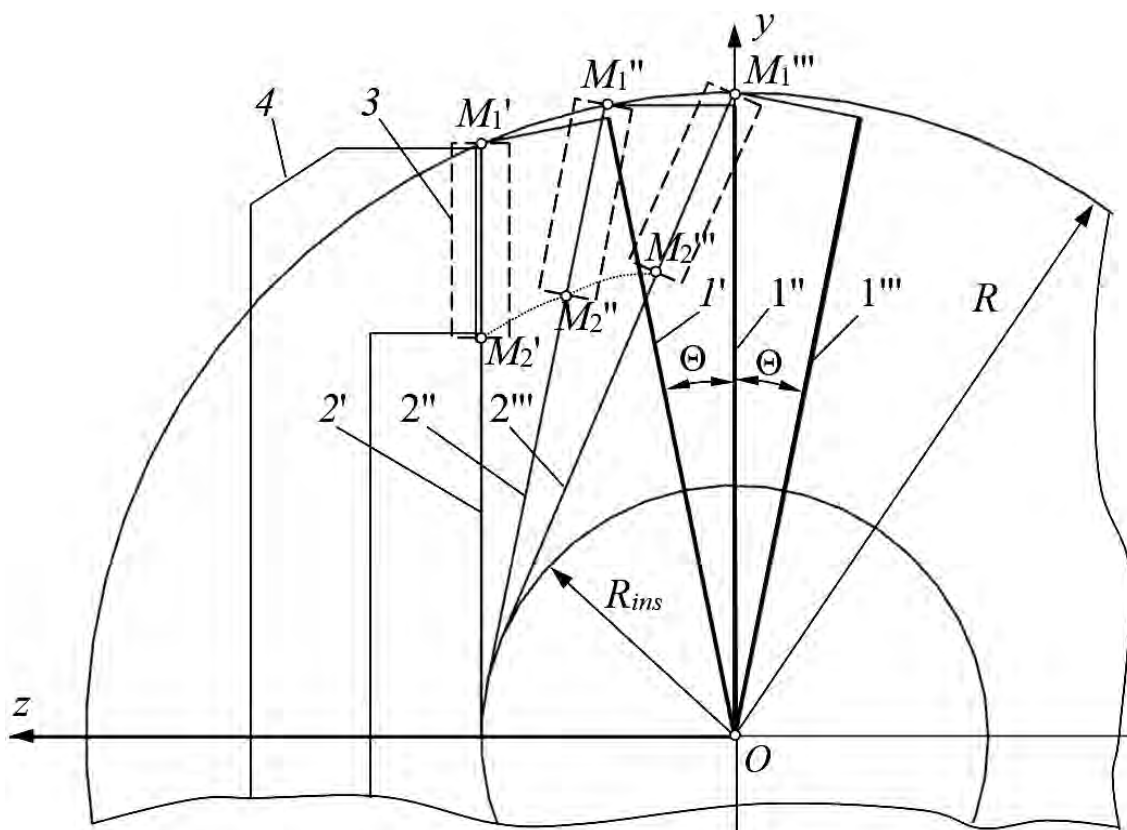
Движение инструмента при изготовлении зубчатого профиля: 1 – сателлит; 2 – ось ролика; 3 – профиль инструмента; 4 – заготовка
